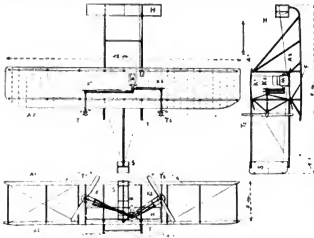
A¹ obere, A² untere Tragfläche. H Schlitten. H Höhensteuer. S Seitensteuer. M Motor. K¹, K² Ketten zum Antrieb der Schrauben T¹, T² (die Pfeile zeigen die Drehrichtung an). Linke Kette gekreuzt. Beide Ketten in Rohren geführt. W Kühlapparat für den Motor. R Benzinreservoir. L¹ Steuerhebel für das Höhensteuer. L² Hebel für das Seitensteuer und Verwinden der Tragflächen.
